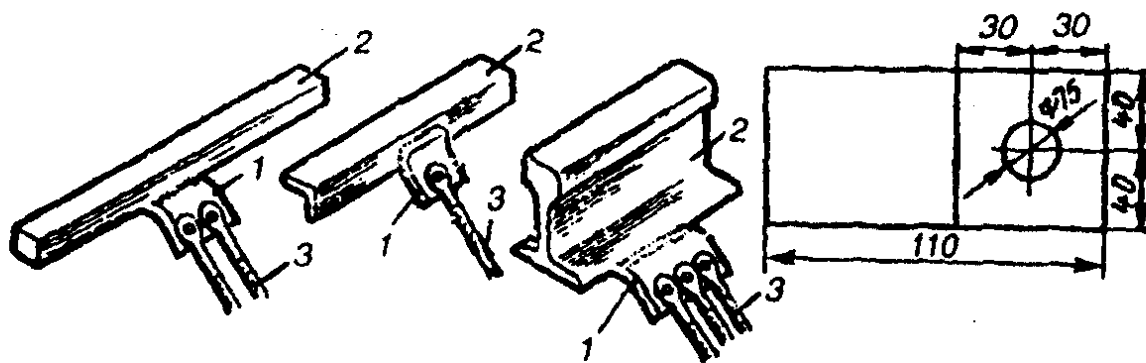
Токопроводящие планки на стальных троллеях:
